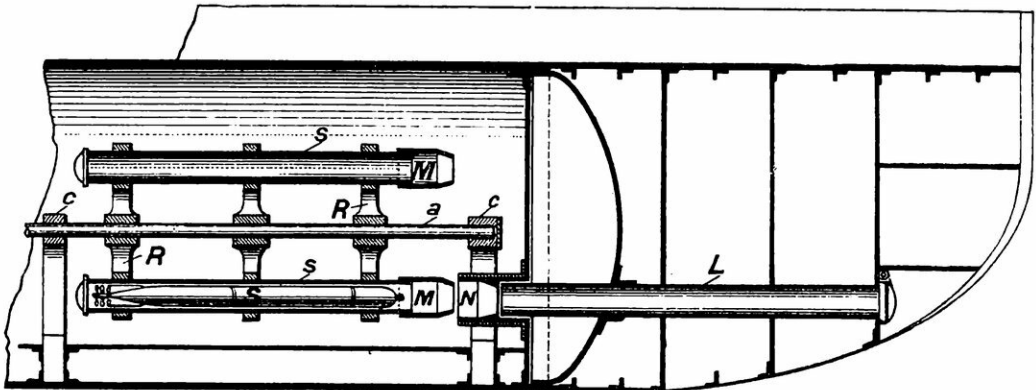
COUPE LONGITUDINALE DE L'AVANT D'UN SOUS-MARIN POURVU DU BARILLET A TORPILLES
